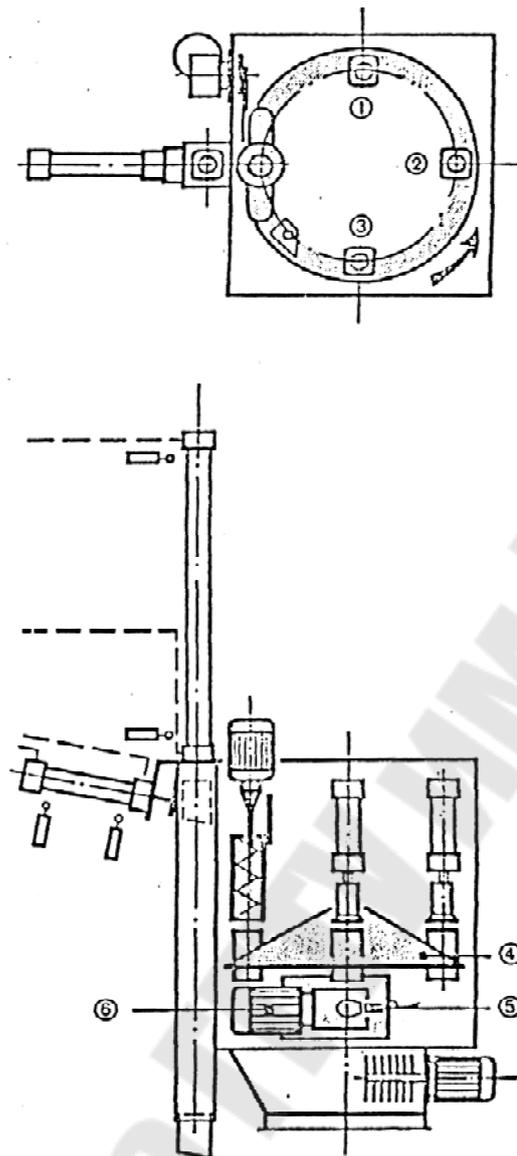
Трехпозиционная установка для автоматического определения требуемой добавки глинистого связующего в формовочную смесь:
